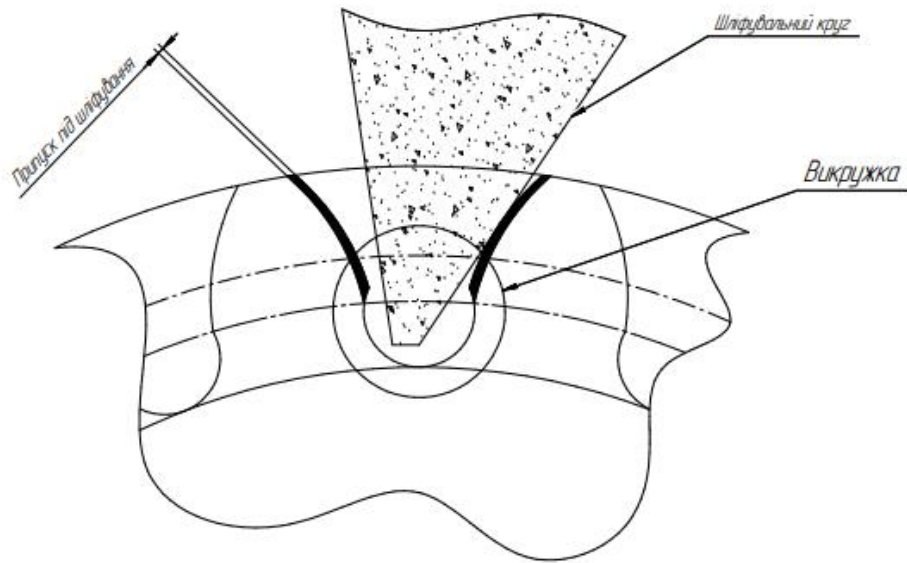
Профіль зубчастого колеса під зубошліфування з викружкою
